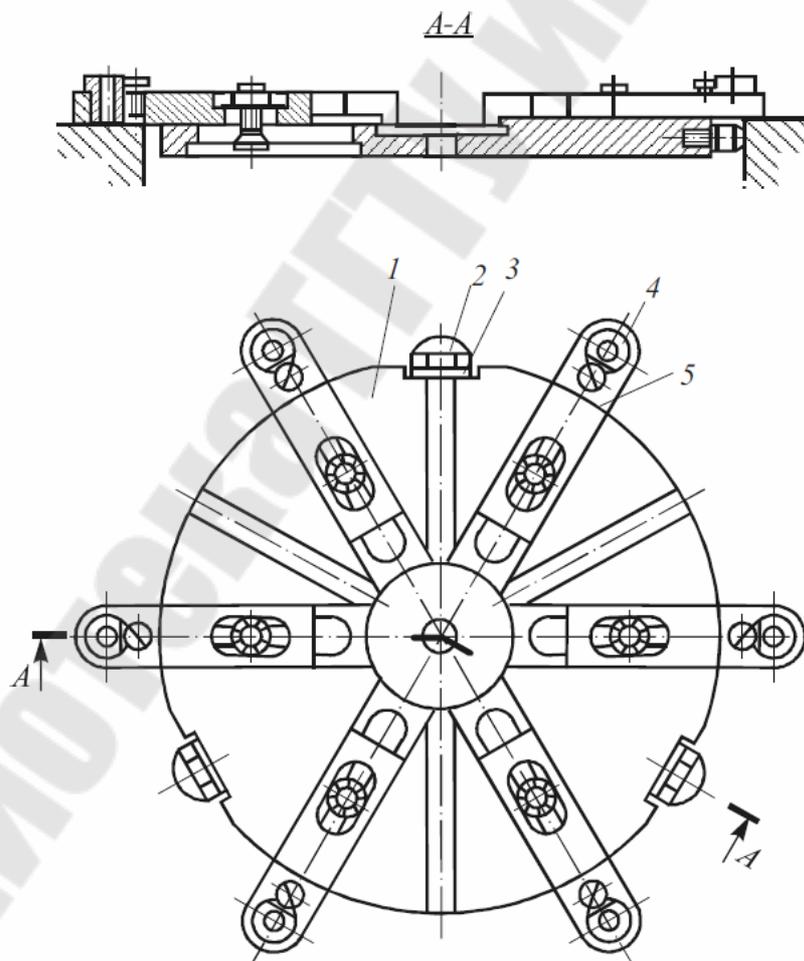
Универсально-сборный накладной кондуктор для сверления шести отверстий [4]
